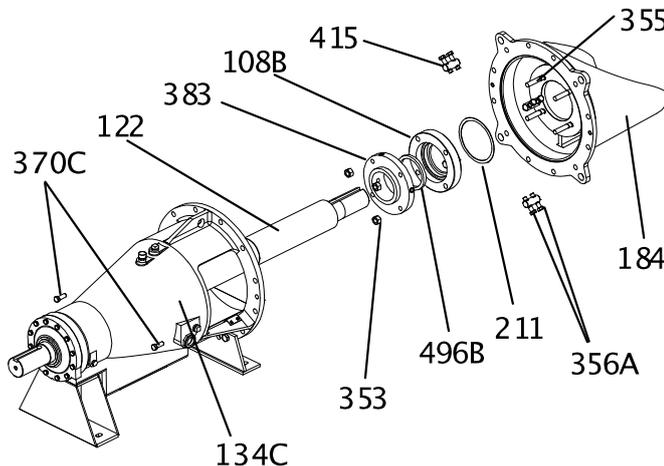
Remontagem de vedação mecânica com adaptador opcional
